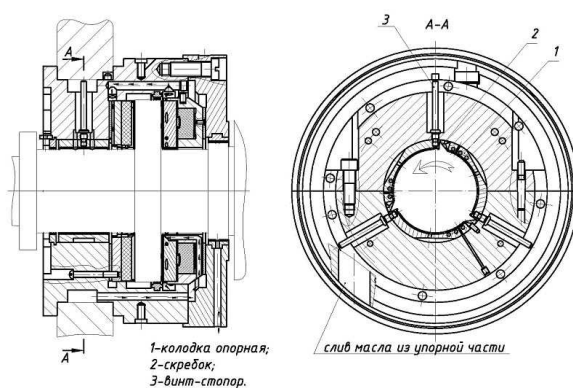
Подшипник опорно-упорный ПДУ-120/260
